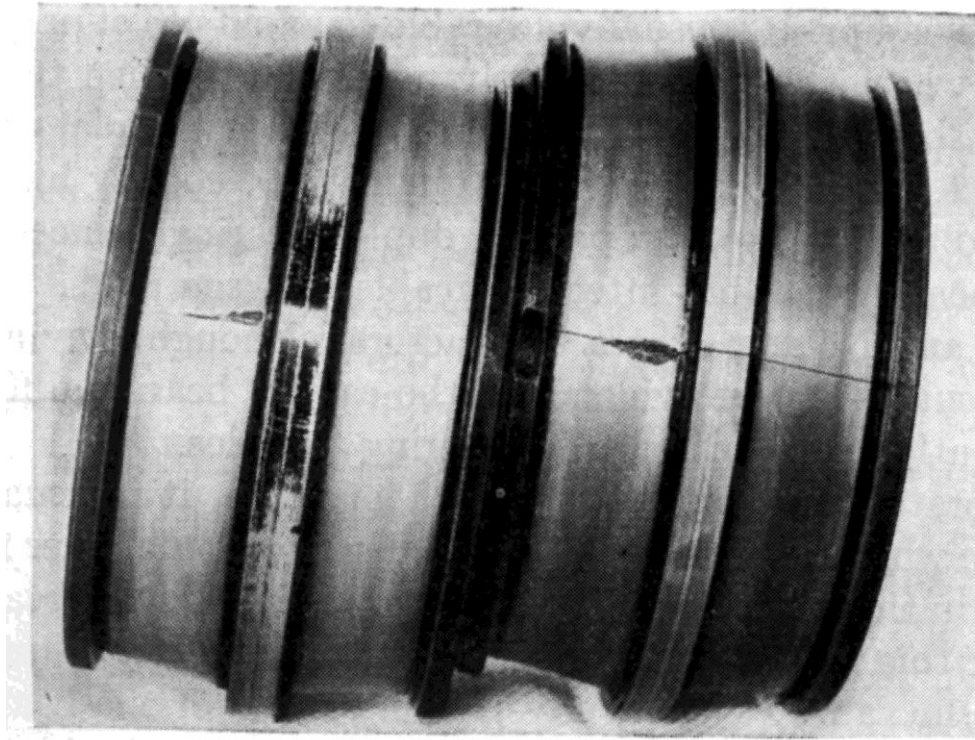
Rotura de pista interior debido a excesiva interferencia de montaje sobre el eje [1]
